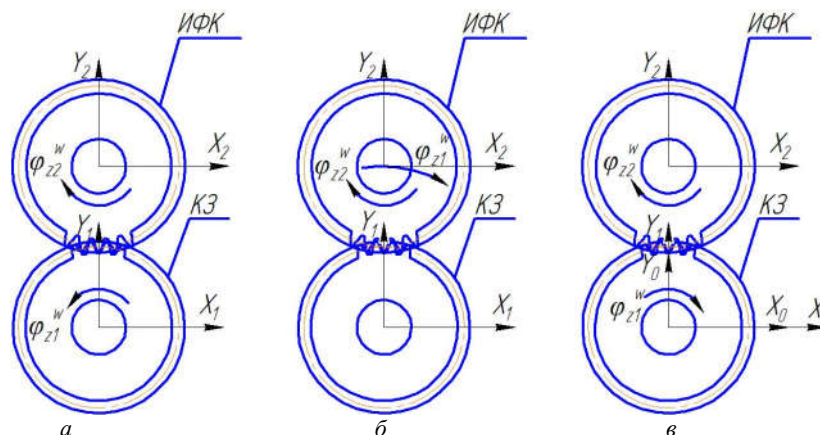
Геометро-кинематические схемы движения исходных формообразующих контуров (ИФК) и контуров заготовок (КЗ) при формообразовании КЗ: а – обозначение абсолютных вращательных движений ИФК и контура заготовки в собственных системах координат; б – обозначение двух вращательных движений ИФК относительно неподвижного контура заготовки по П.Р. Родину; в – обозначение двух вращательных движений ИФК относительно неподвижного контура заготовки, согласно теории отражения аффинного пространства [16]
